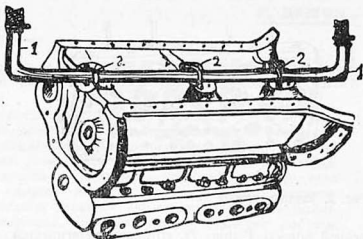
Установка охлаждающей трубы в подшипнике блока мотора
